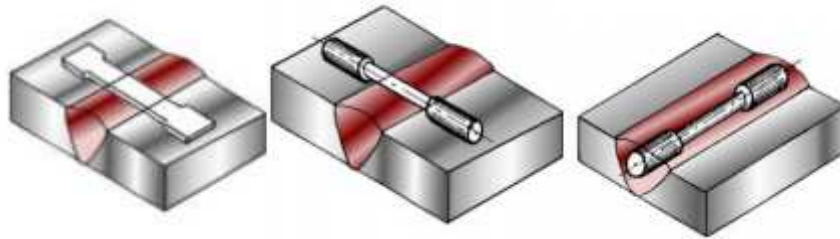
Sens possibles du prélèvement des éprouvettes de traction sur un cordon de soudure.
